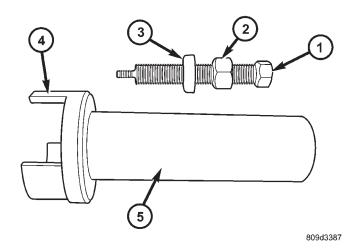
Instalador insertador 8680 y conjunto de tornillo de herramienta 8422
